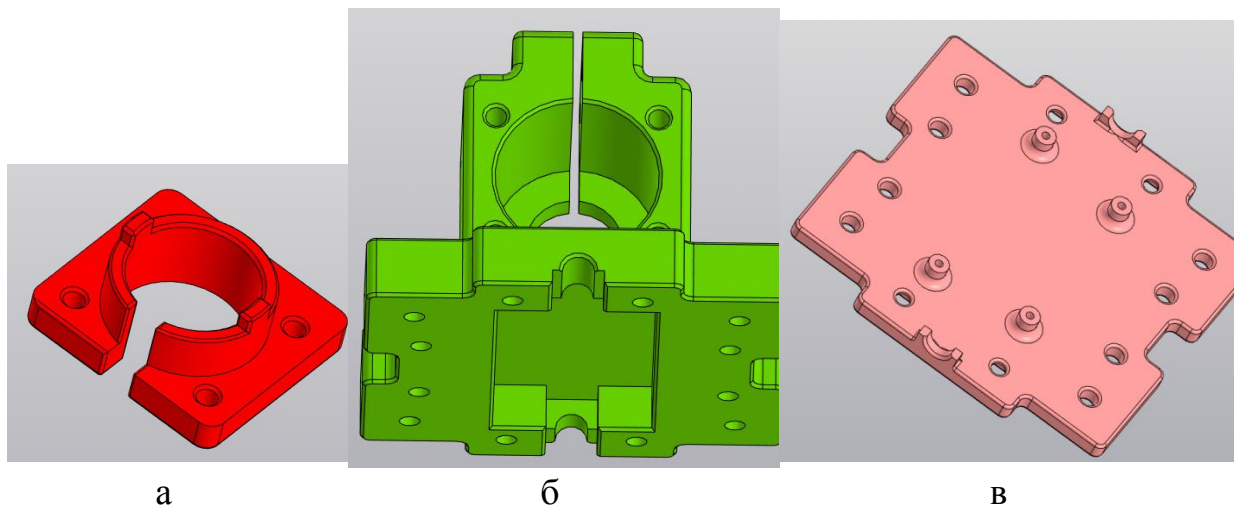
Детали крепления: а – крышка; б – корпус; в – основание
